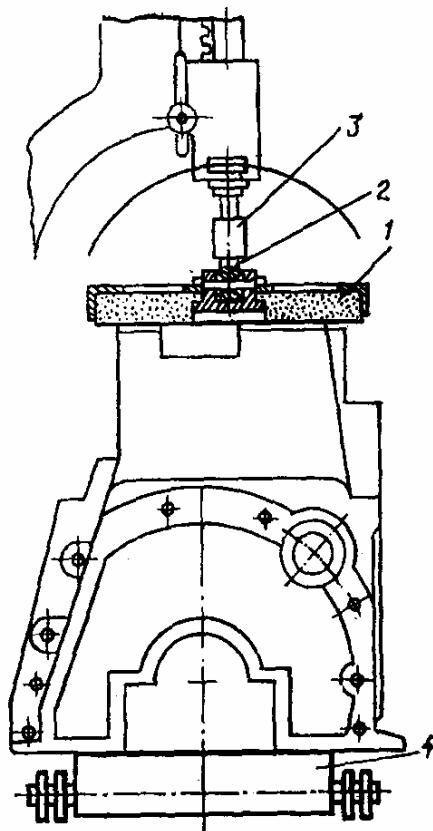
Пристрій для шліфування привалкової поверхні блока циліндрів на свердлильному верстаті:
